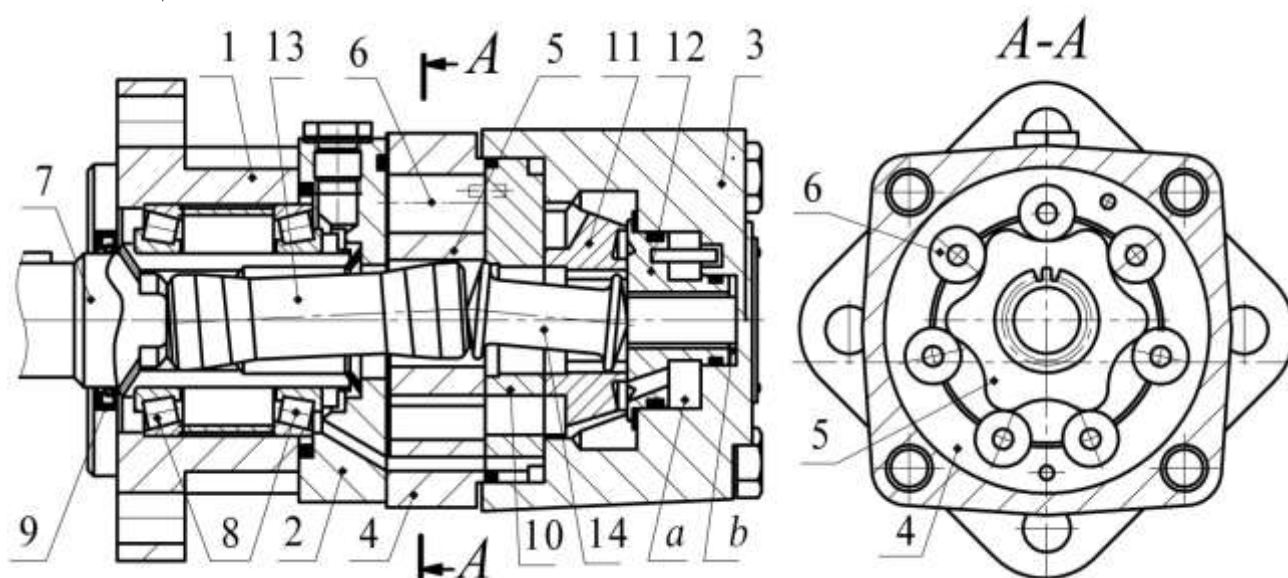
Героторний гідромотор: а – поздовжній; б – поперечний розрізи
